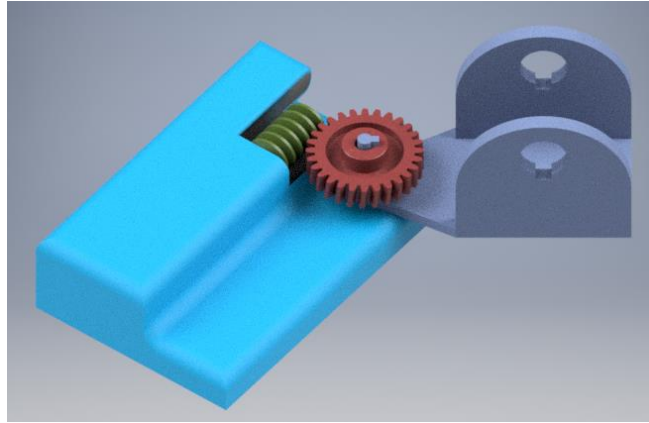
Ensamblaje engranajes flexión-extensión.
